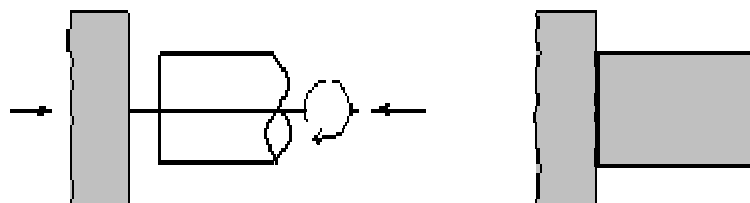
Зварювання тертям в стик, заготовки та колеса турбіни
